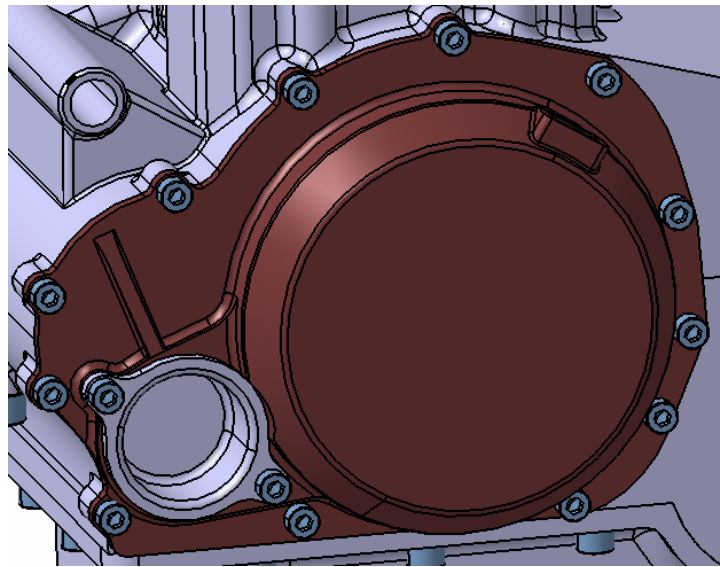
Pravé víko bloku motoru s krytem spojky a čerpadlem chladicího okruhu
